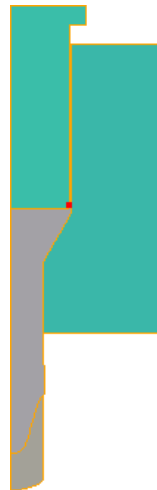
Формоутворення біметалевої заготовки -
